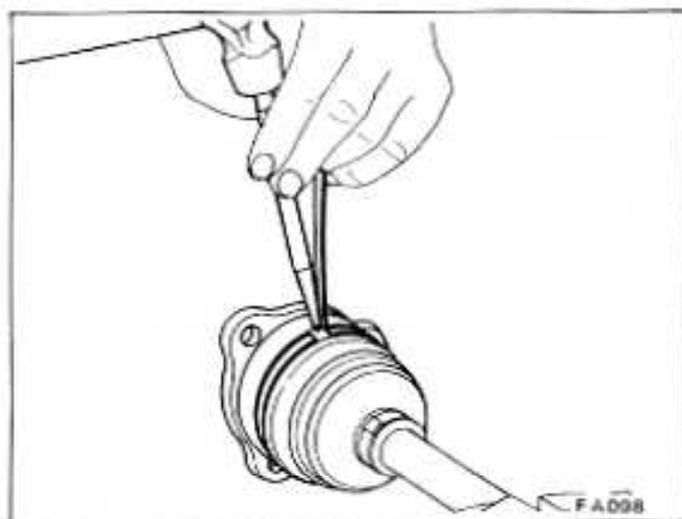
Fixation définitive du collier de manchon caoutchouté
